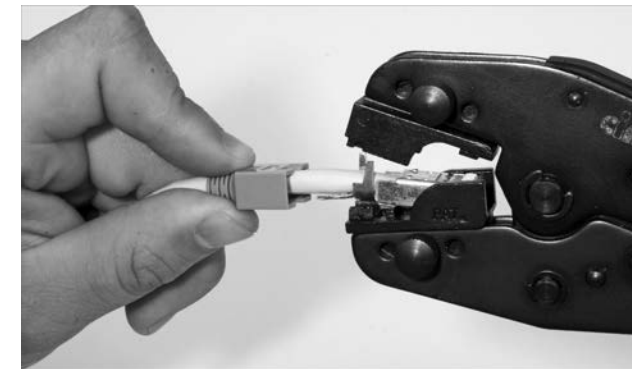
Einführen des RJ45-Steckers in das Crimpwerkzeug
